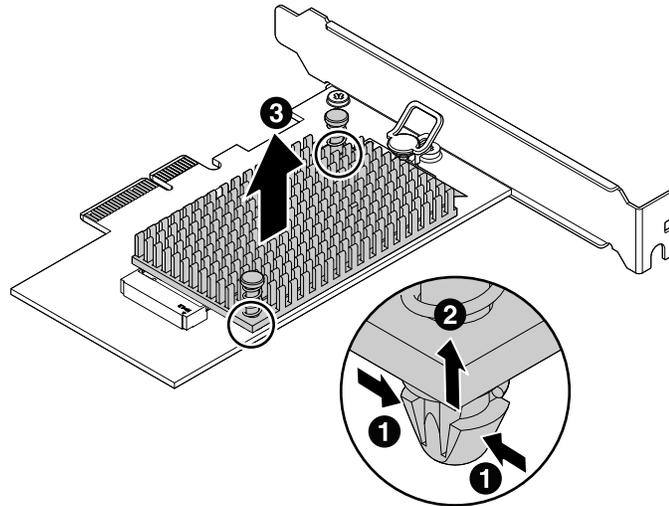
Kühlkörper vom Adapter für das M.2-Solid-State-Laufwerk entfernen
